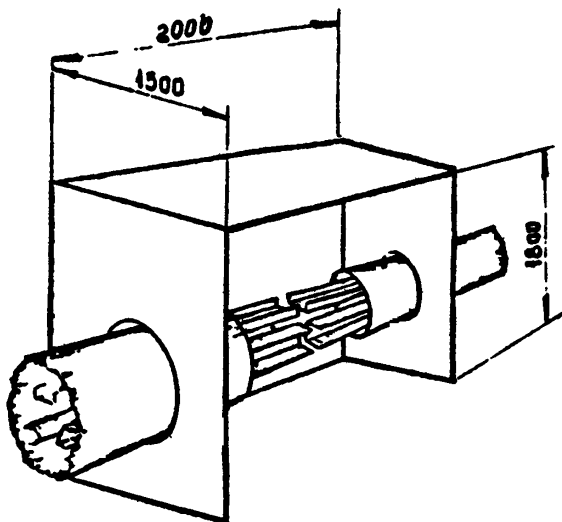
Кабина сварщика для сварки стыков токопровода
